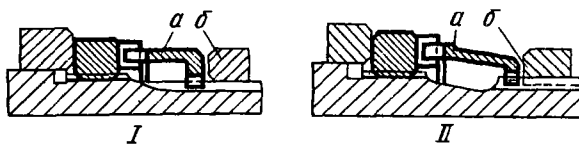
Фиксация кольцевой гайки с торцовыми зубьями на ступенчатом валу втулкой, сцепленной с пазом (I) или шлицами (II)
